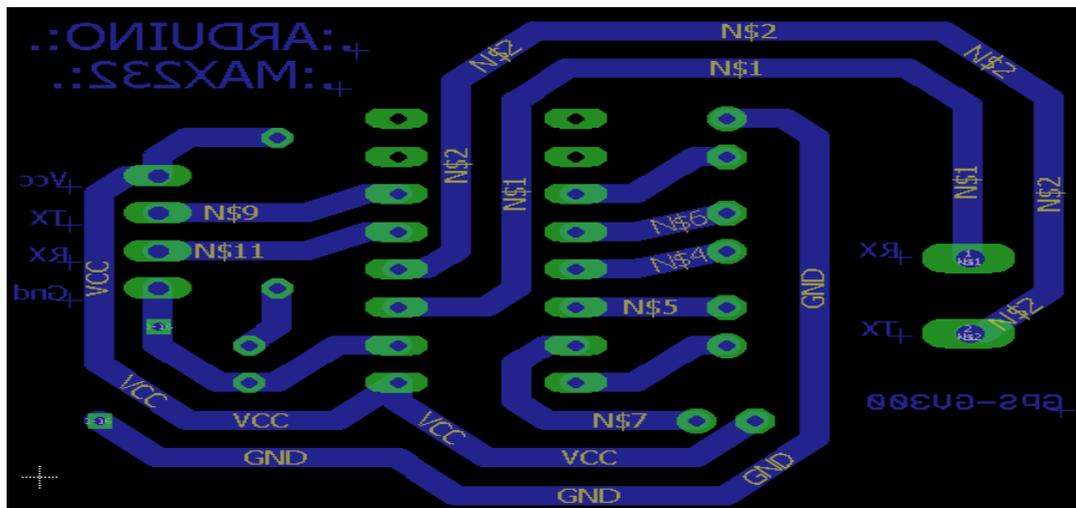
13: Diseño PCB de circuito Conversor TTL a RS232
